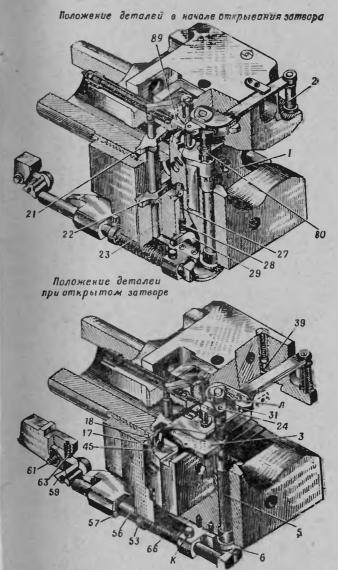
Затвор Д10-ТГ и Д10-Т2С в собранном виде (расположение деталей на 1- клнн; 2- рукоятка затвора; 3- кривошил с роликом; 5- ось кривошила; 6- кулачок по нижний выбрасыватель; 23- ось выбрасывателя; 24- рычат закрывающего механизма; 27- щелка рукоятки; 39- стопор упора; 45- ось предохранитель; спуска, 53- кольцо; 56- скалка: ограничитель рукоятки; 80- ось повториого взвода;
